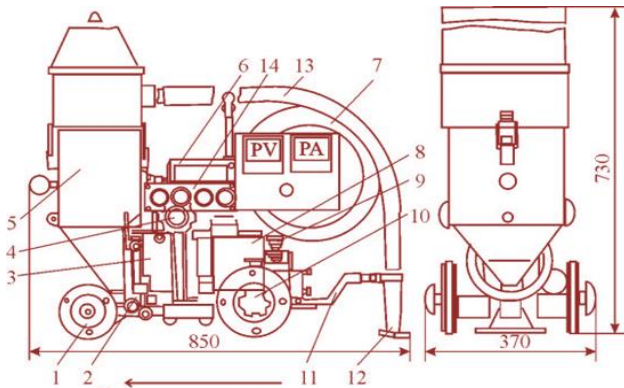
Напівавтомат для наплавлення під шаром флюсу:
